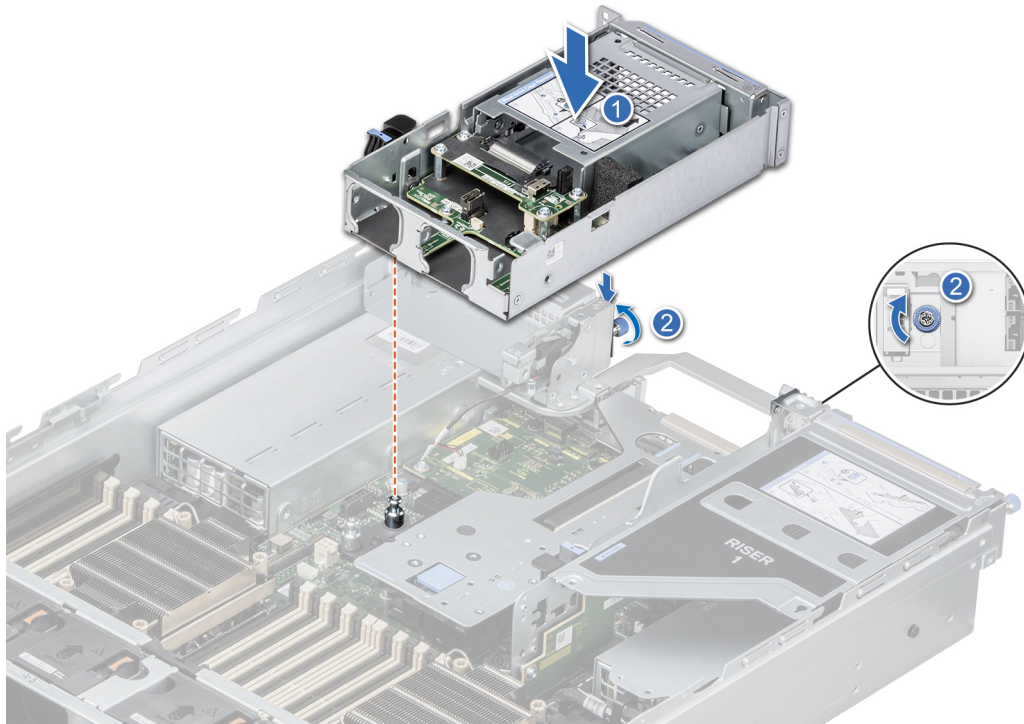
Installation du module de disques arrière 2 x 2,5 pouces
